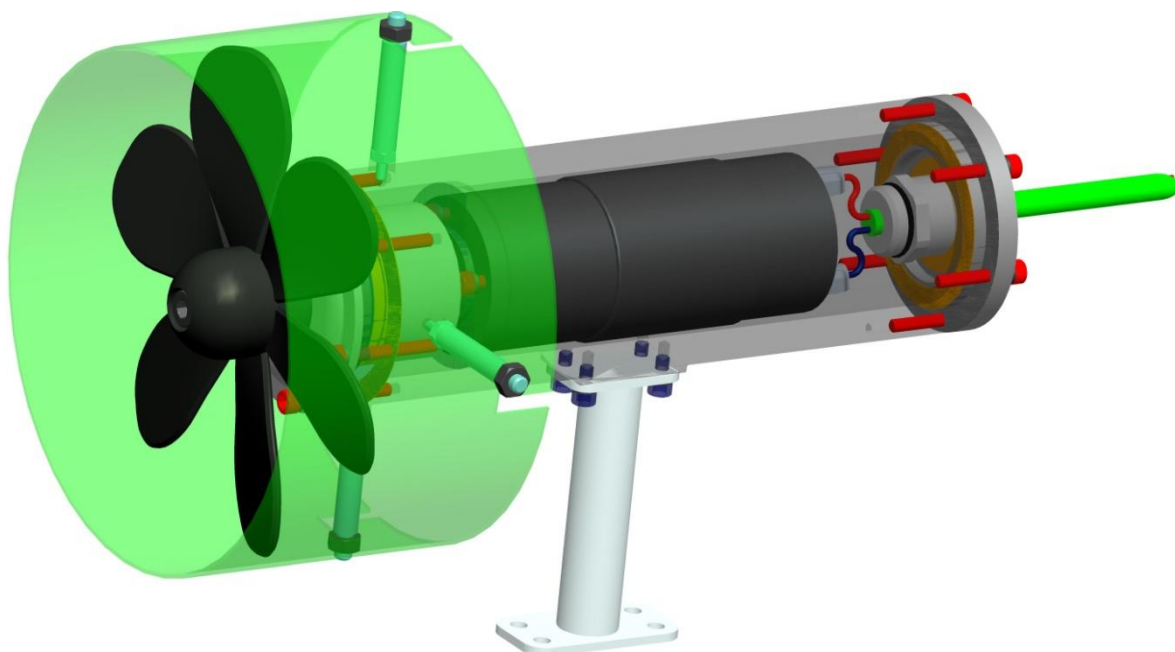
Spojení pohonu s robotem - 3D-model Pro/E
